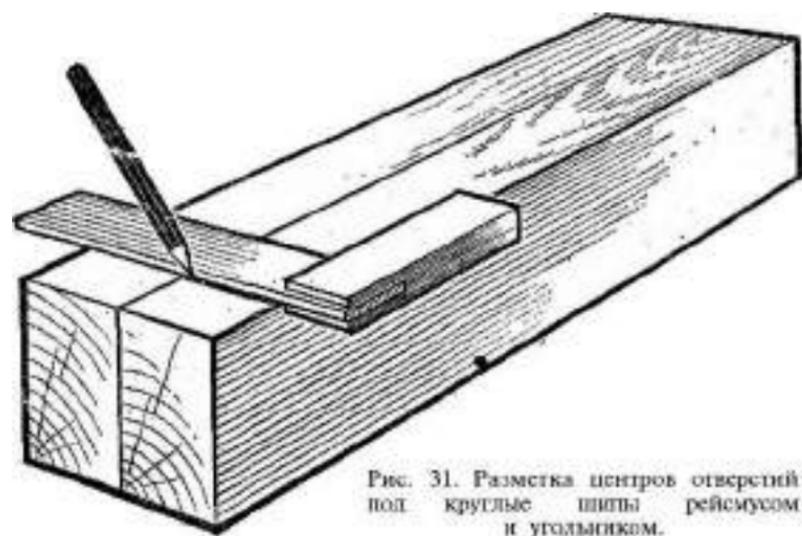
Разметка центров отверстий под круглые штыи рейсмусом и угольником.
